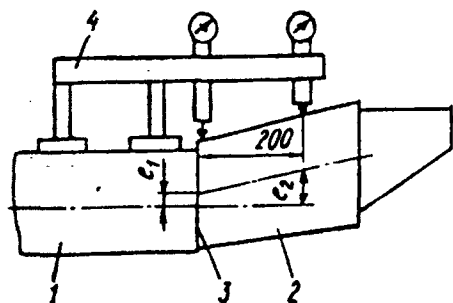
Измерение отклонений от соосности при сварке труб. 1,2 - свариваемые элементы, 3 - сварной шов, 4 - накладное измерительное приспособление.
